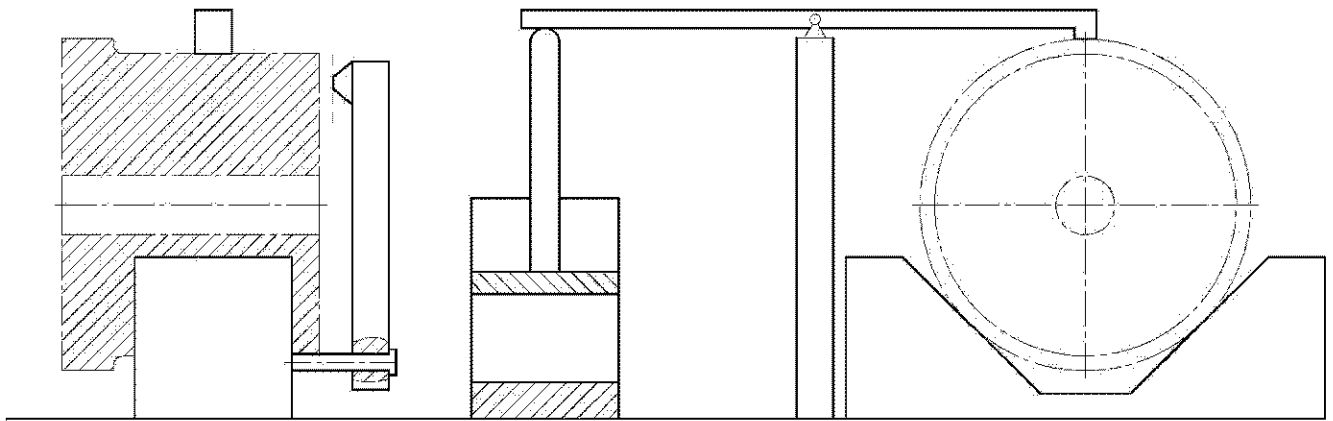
Результаты разработки схемы закрепления заготовки в станочном приспособлении
